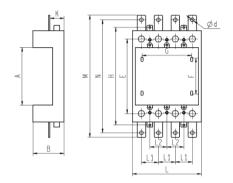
Габаритные размеры корзины втычного фронтального подключения КА-300
